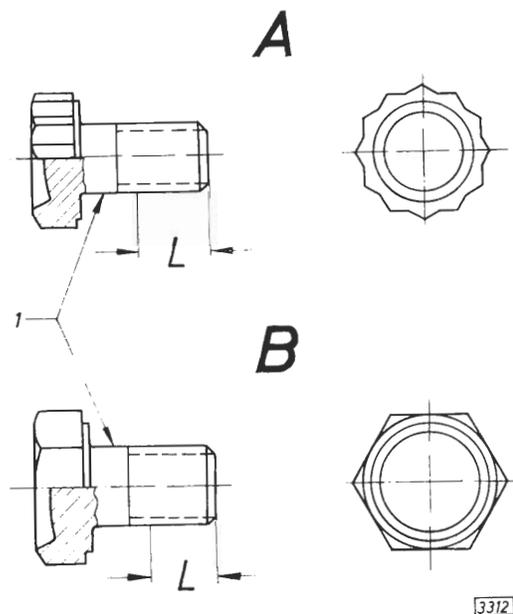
Ausführungen von Schrauben zur Befestigung des Tellerrades an das Ausgleichgehäuse
